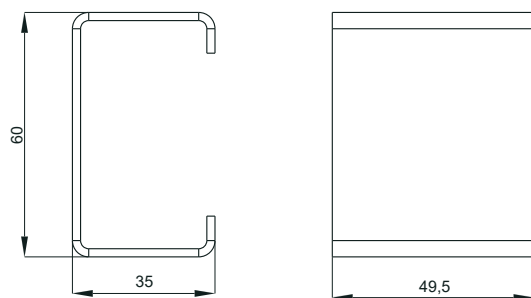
Распорка для П-образного профиля / Figure I.3 – Spacer for U-shaped profile
